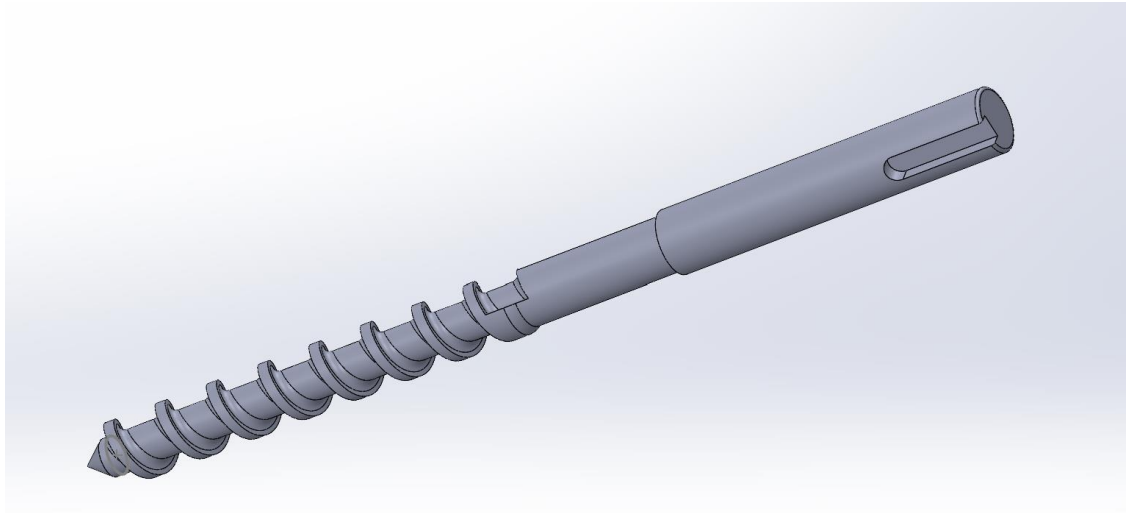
Готова 3D-модель набивного шнека живильника
